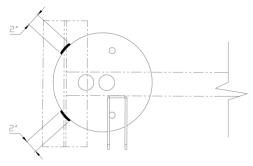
Cordones de soldadura soporte superior de bolsa
